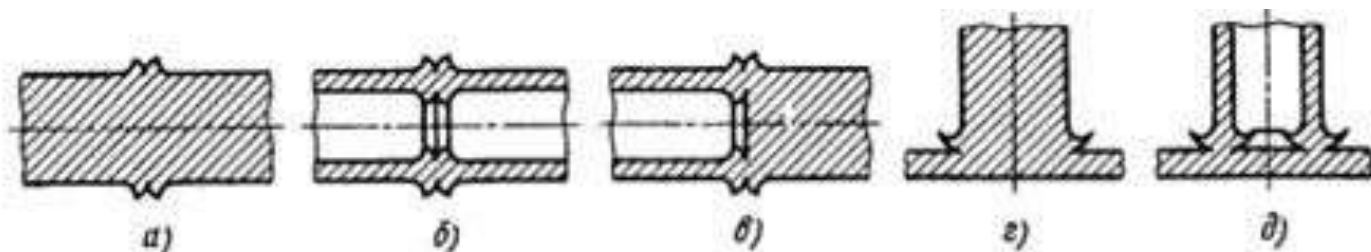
Типы соединений, выполняемых с помощью сварки трением:
